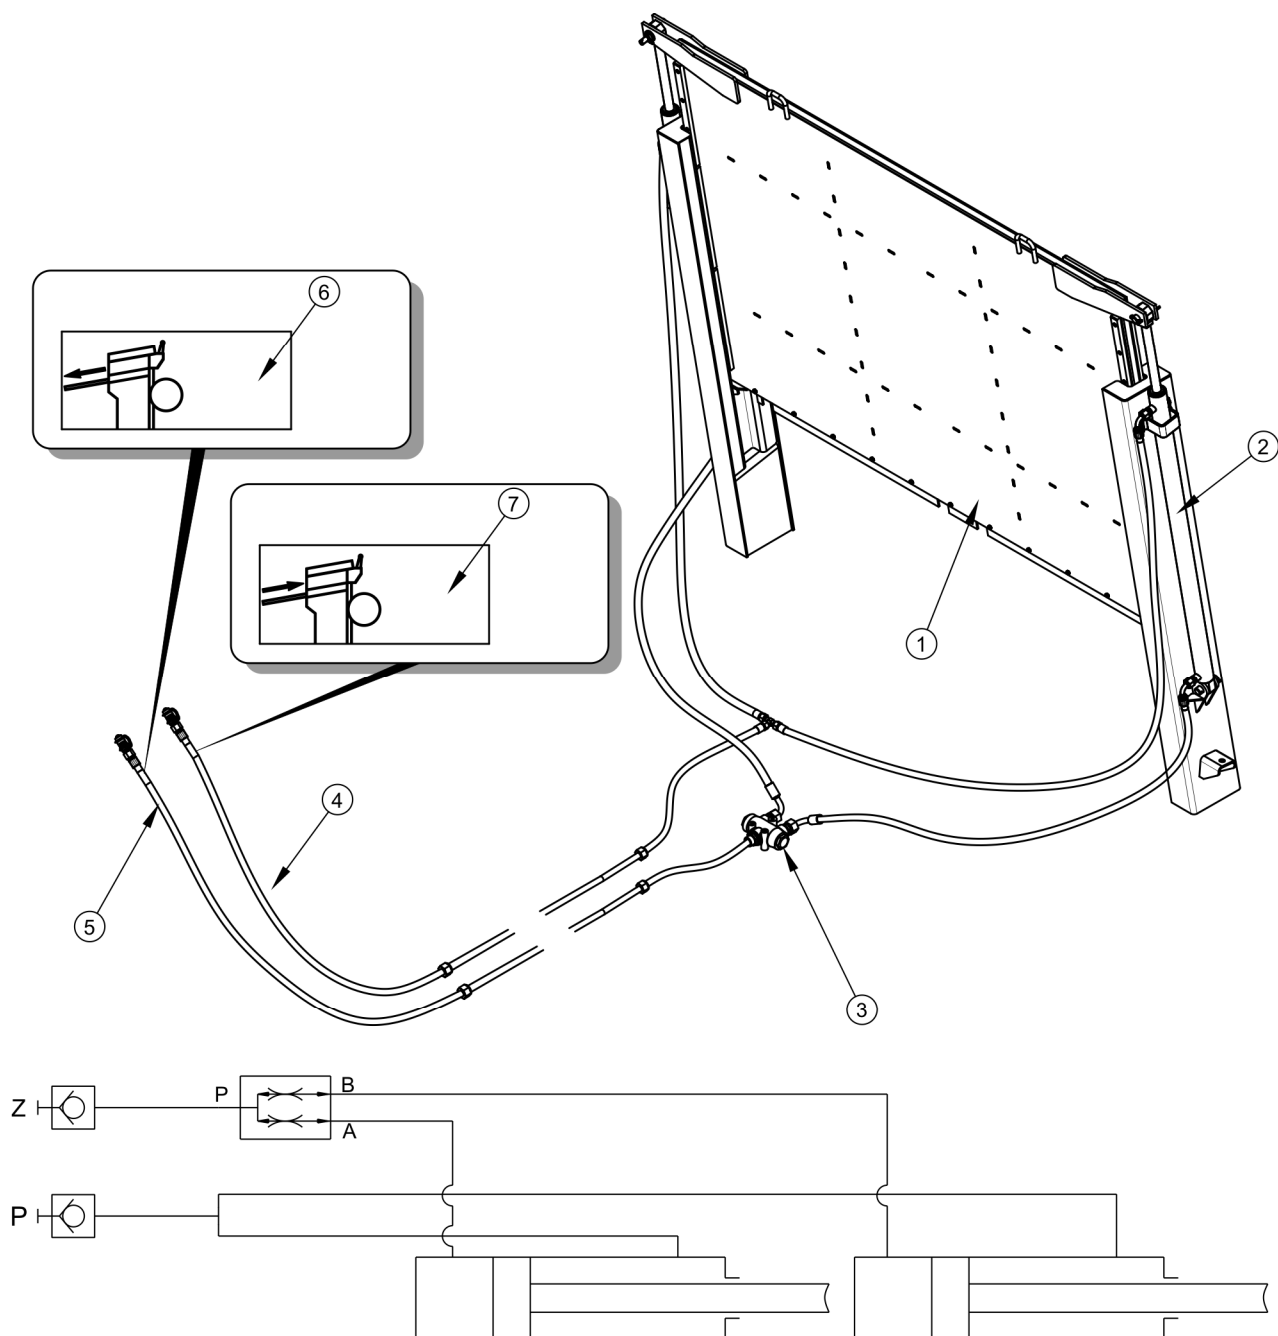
Konstrukce a schéma hydraulické instalace zadního poklopu
